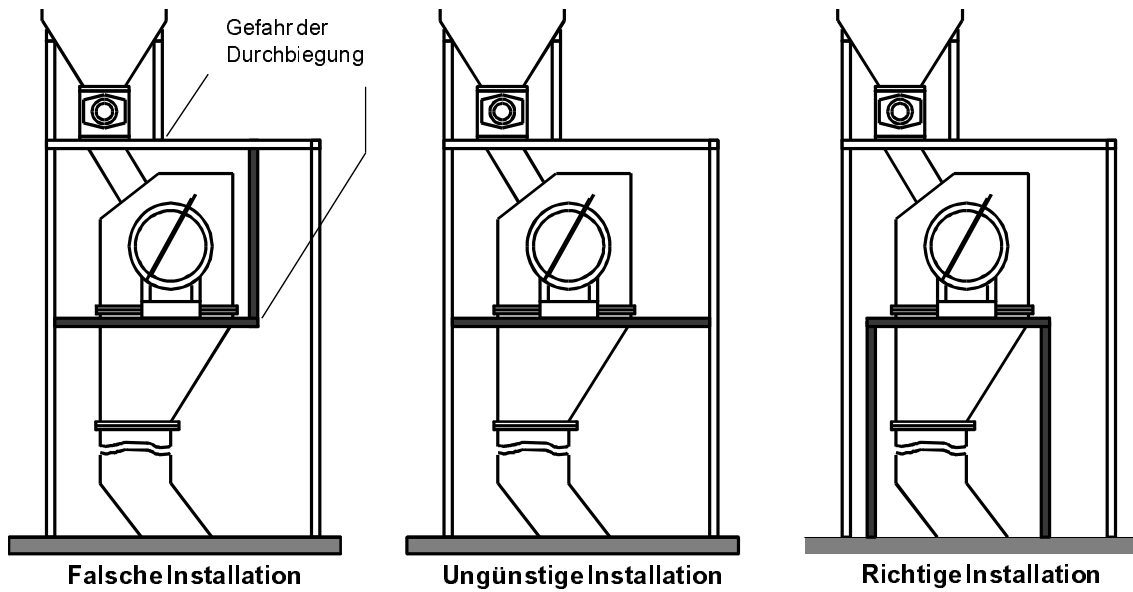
Bauseitige Unterkonstruktion für den Prallplattensensor
